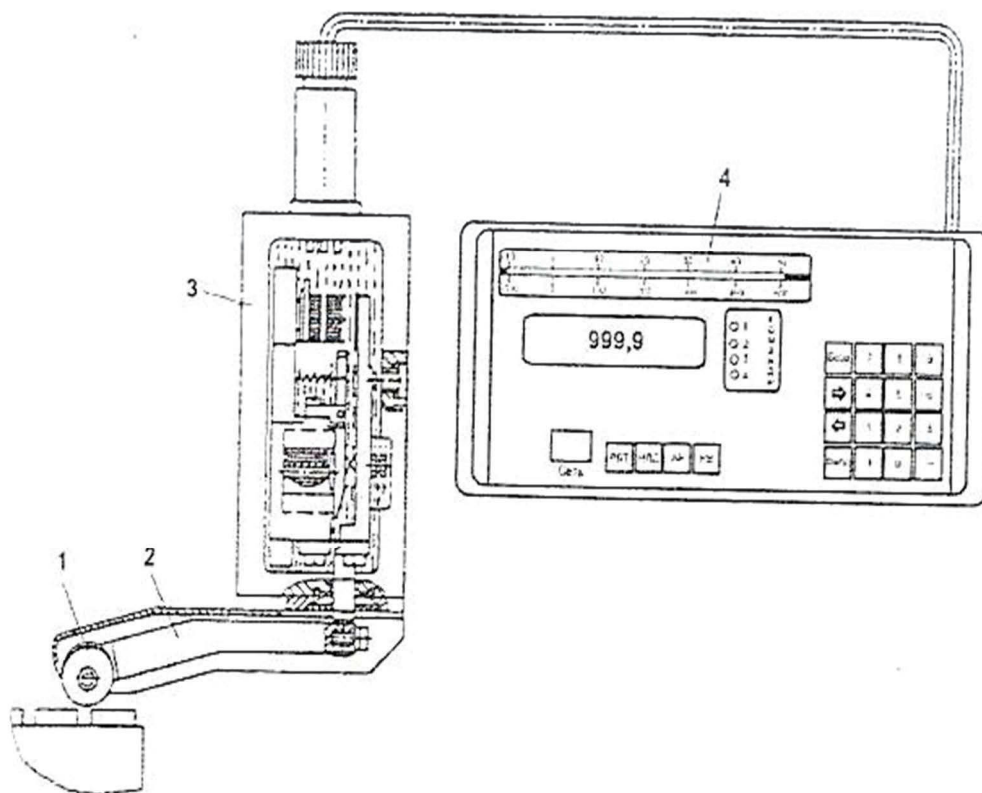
Индуктивный прибор БВ-4308: 1 – измерительный наконечник; 2 – измерительный рычаг; 3 – индуктивный преобразователь; 4 – электронный блок
